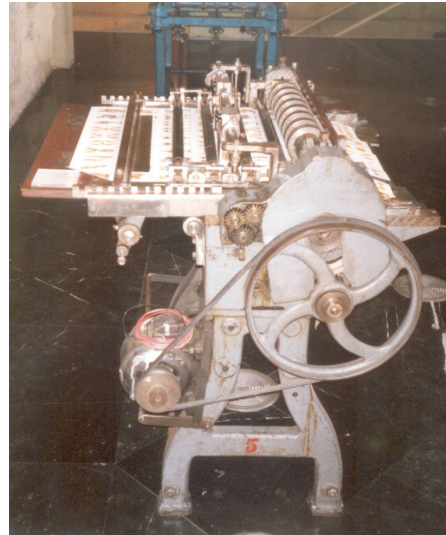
Máquina de cuchillas circulares a motor, 1880
